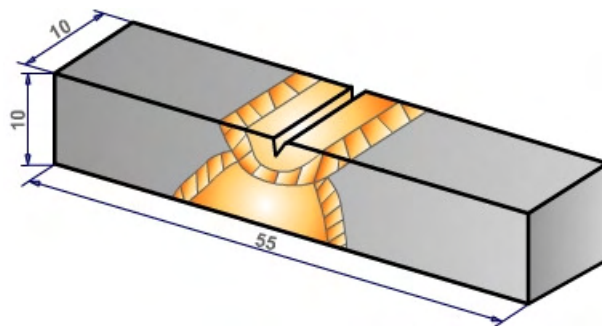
Desenho esquemático do corpo-de-prova para ensaio de impacto Charpy. Dimensões em mm.
